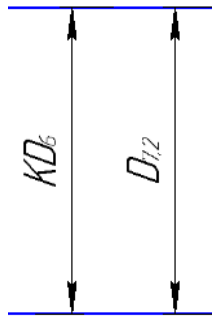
Размерная цепь для обработки отверстия $R55^{(-0,74)}$.
